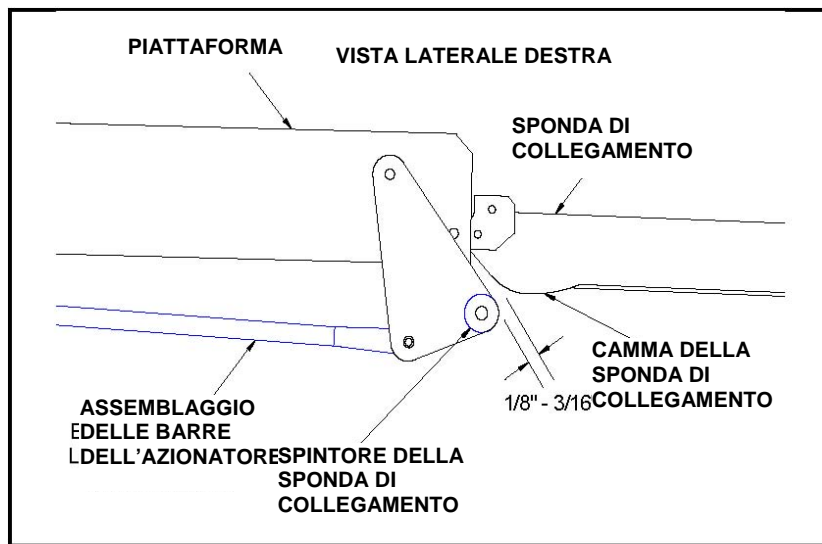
REGOLAZIONE DELLA PIASTRA DI FISSAGGIO
